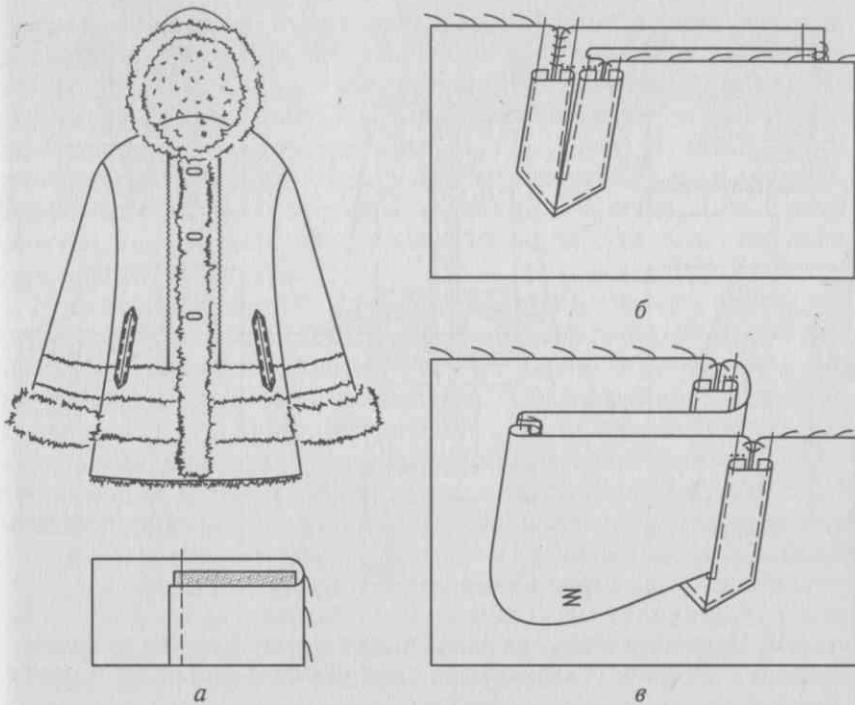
Поузловая обработка двусторонней куртки из мехового велюра:
